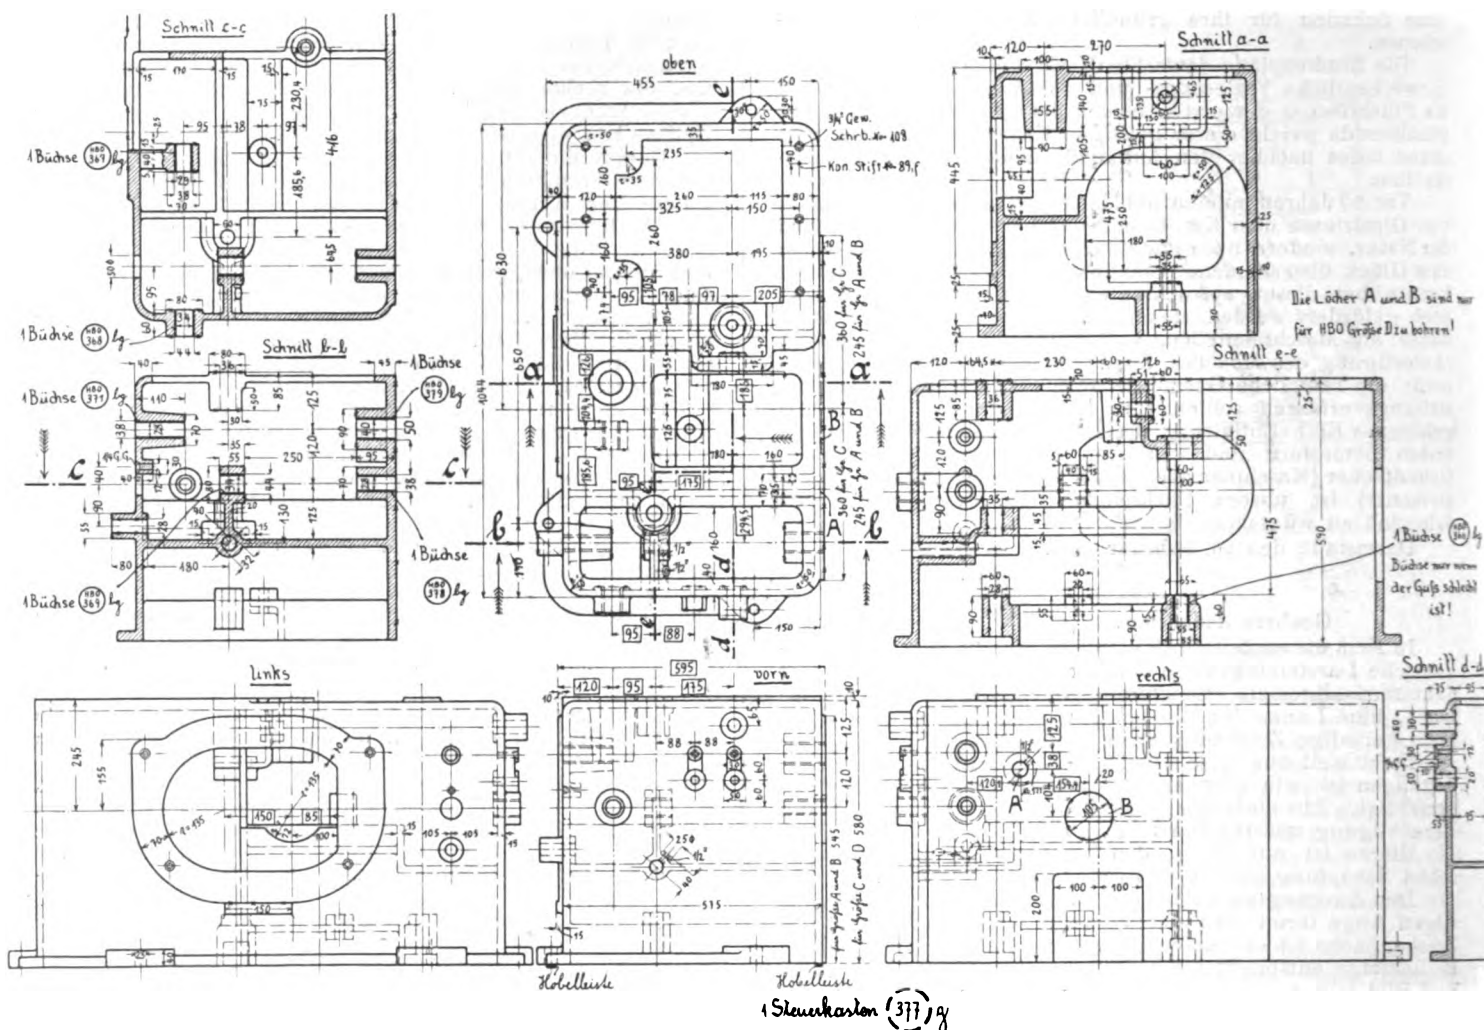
Werkstattzeichnung der Werkzeugmaschinenfabrik Union.
